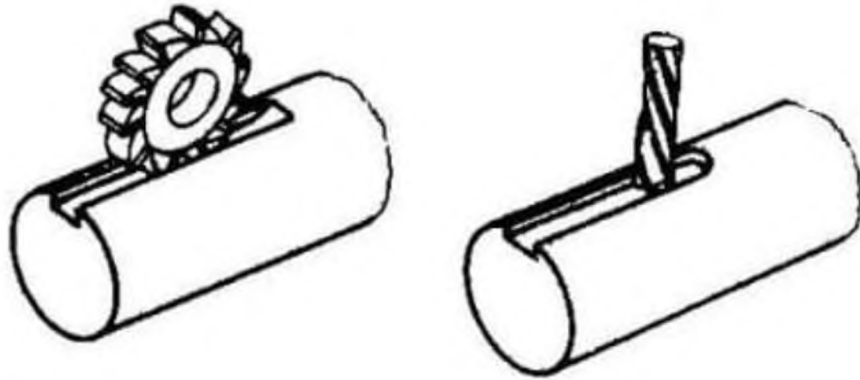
Умовні схеми фрезерування шпонкових пазів
